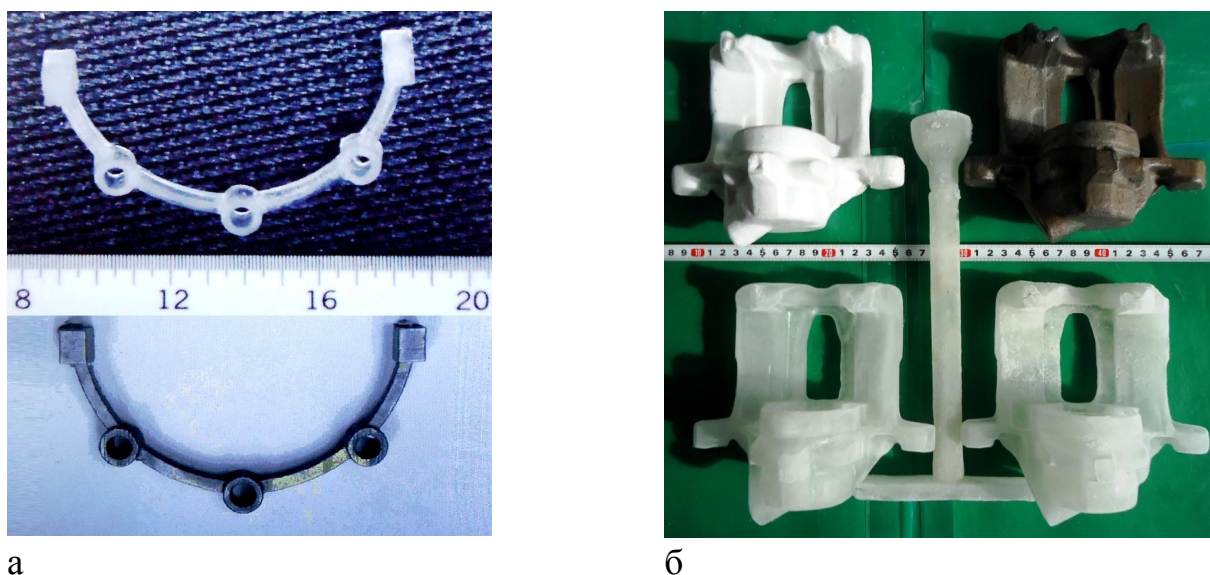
Модели и отливки: а - ЛМ и отливка дуги; б – ПМ, отливка суппорта и блок ЛМ с литниковой системой
